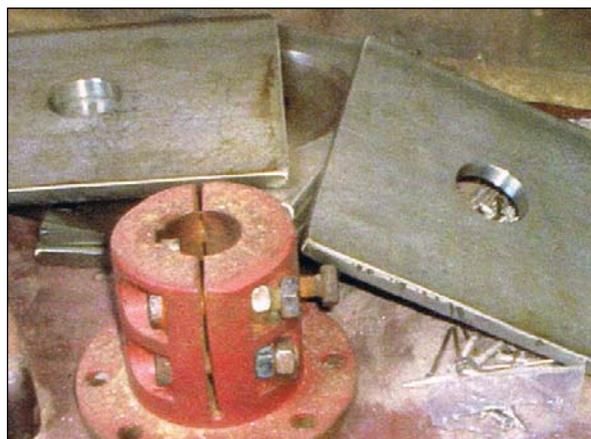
Platinas de la orza y plato de motor. Fuente: autor
